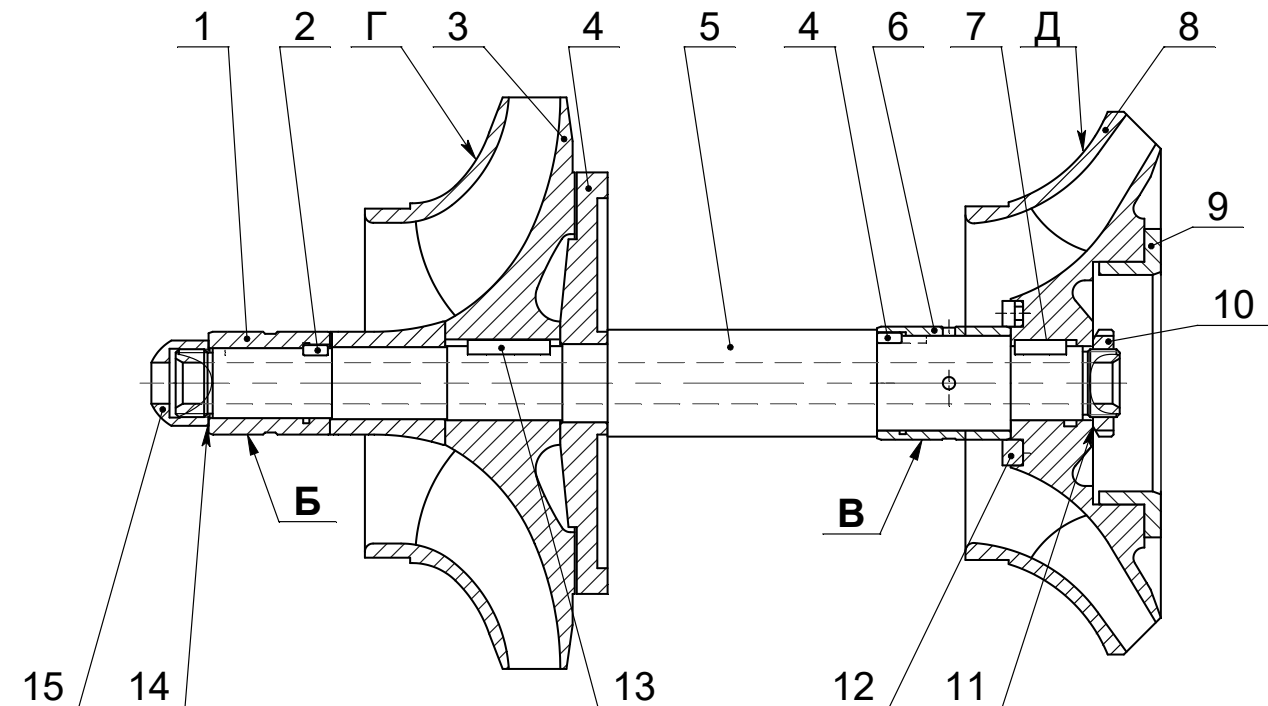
Вал тихоходной части в сборе с колесами для поставки в качестве ЗИП
